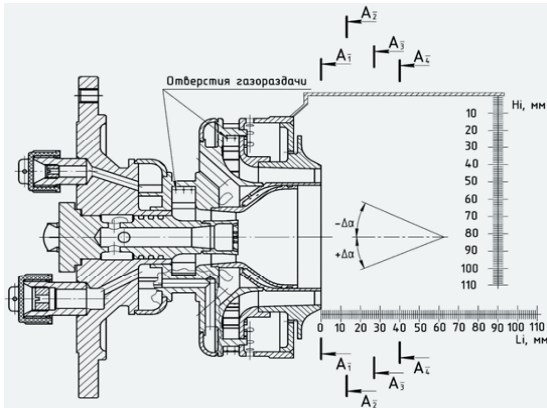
Конструктивная схема низкоэмиссионного горелочного устройства и схема замеров в сечениях
